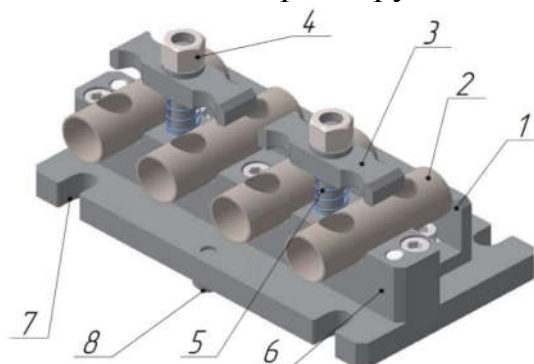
Пристосування для одночасної обробки 4-х труб:
